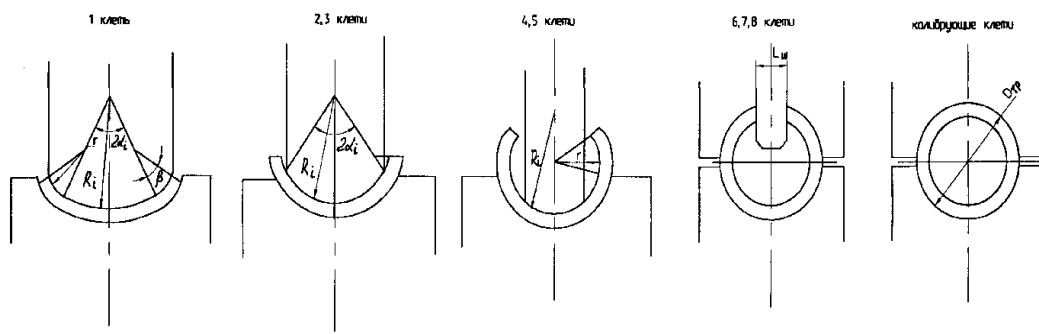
Схема формоизменения поперечного сечения трубной заготовки в процессе валковой формовки на примере калибровок, применяемых на ТЭСА ОАО «Северсталь».
